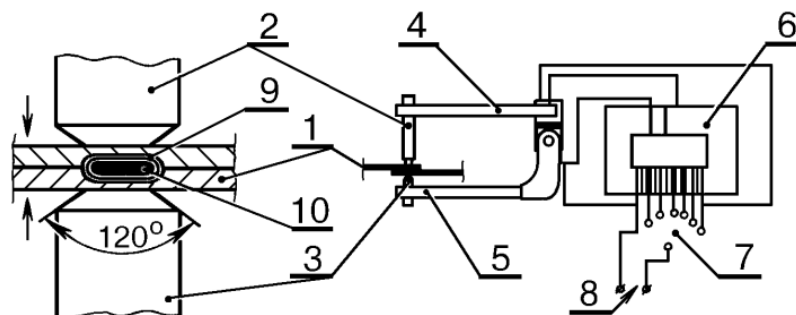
Принципи роботи апарату точкового зварювання:
